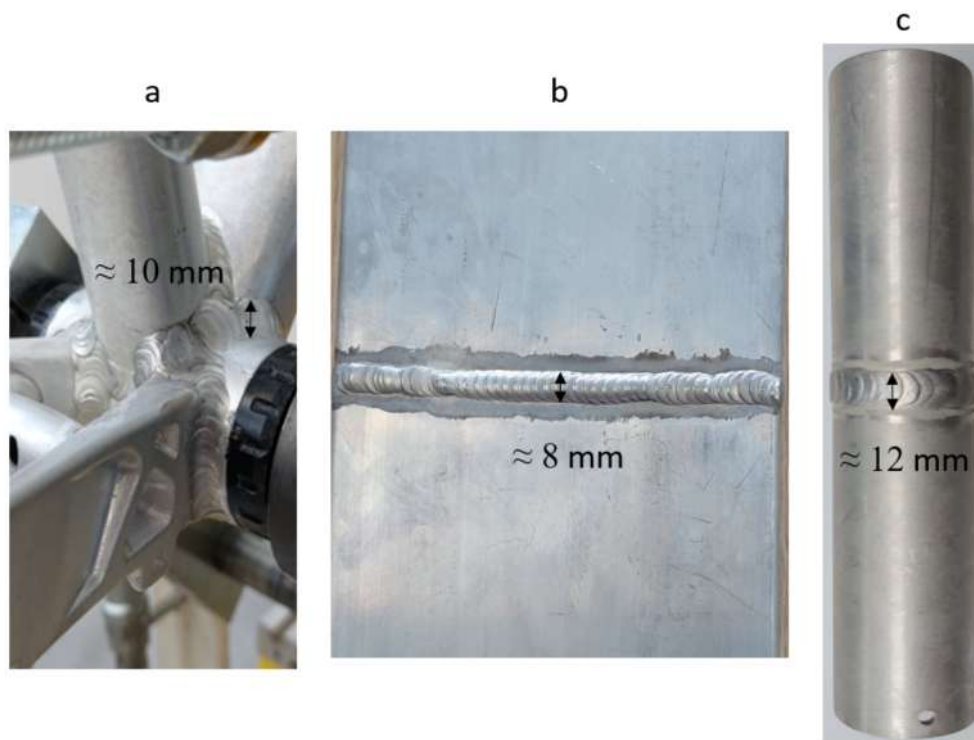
Exemple de géométrie de différents cordons de soudure. (a) au niveau du boîtier de pédalier d'un cadre de vélo, (b) sur un deck de trottinette et (c) sur des tubes soudés bout à bout.
